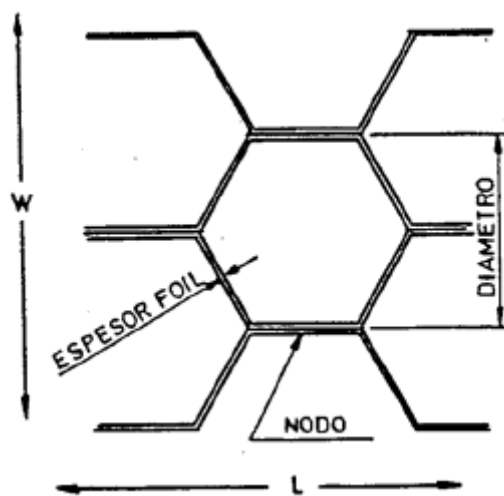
8 Características constructivas estructura tipo sandwich. [1]
